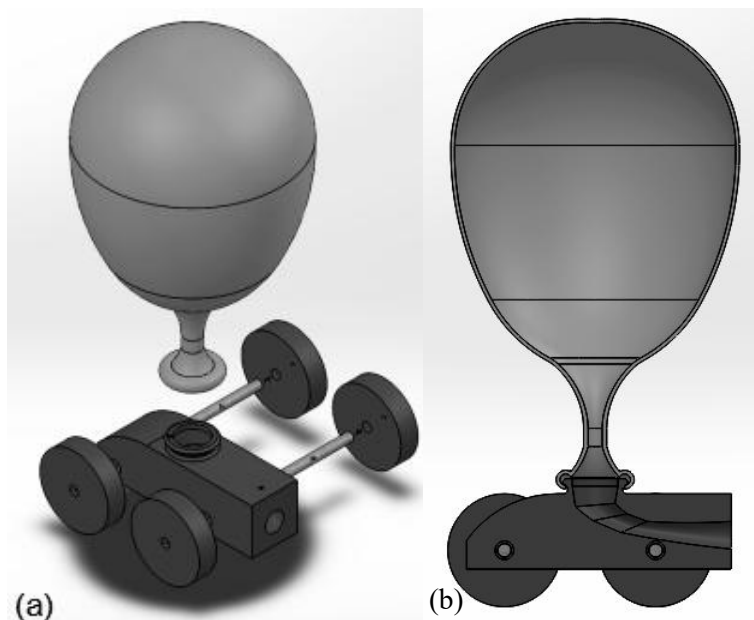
Carrinho apresentado no desafio (a) Vista explodida isométrica, (b) Vista lateral
